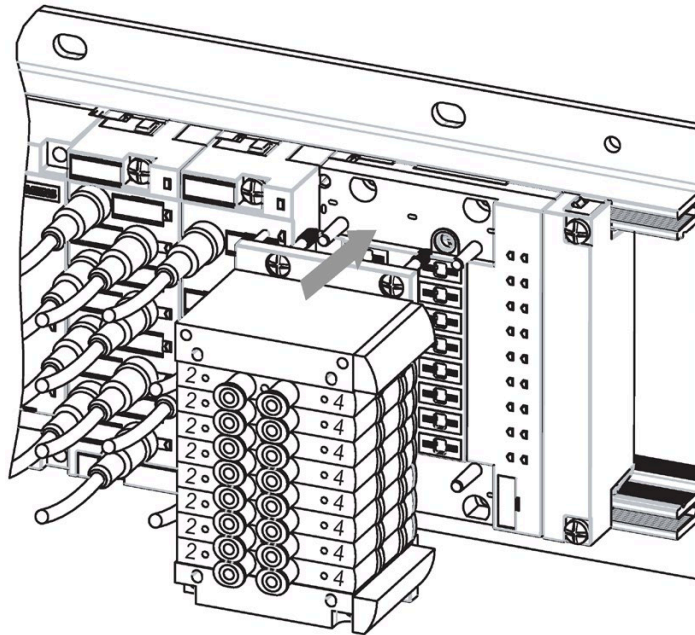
Montage der FESTO-Ventilinsel auf dem Pneumatik-Interfacemodul
